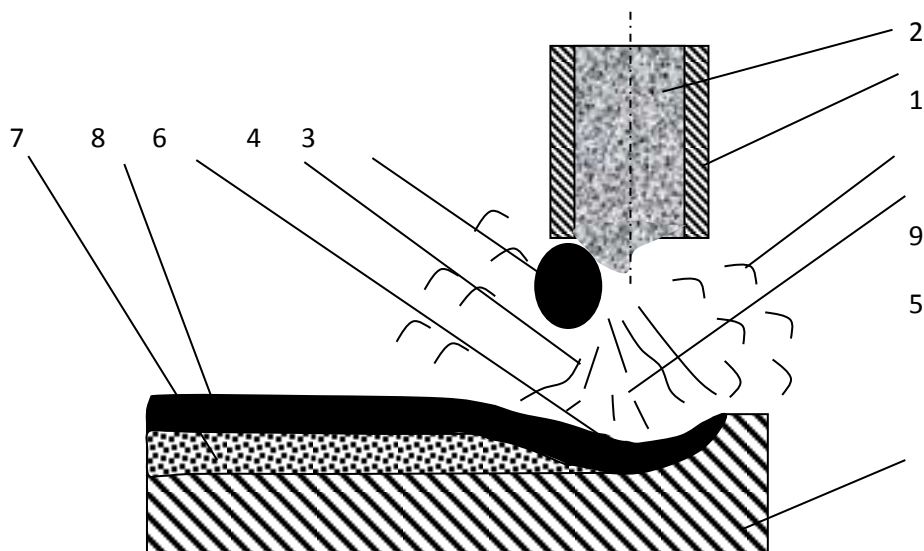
Схема процесса сварки самозащитной порошковой проволокой
